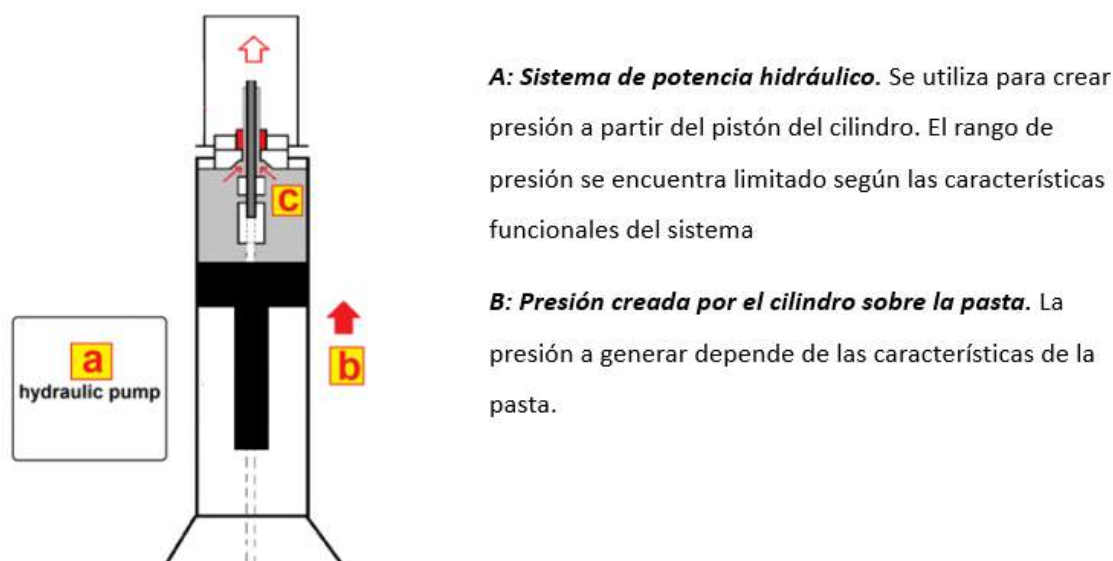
Parámetros importantes en el diseño de extrusores de pistón hidráulico para fabricación de electrodos de soldadura
